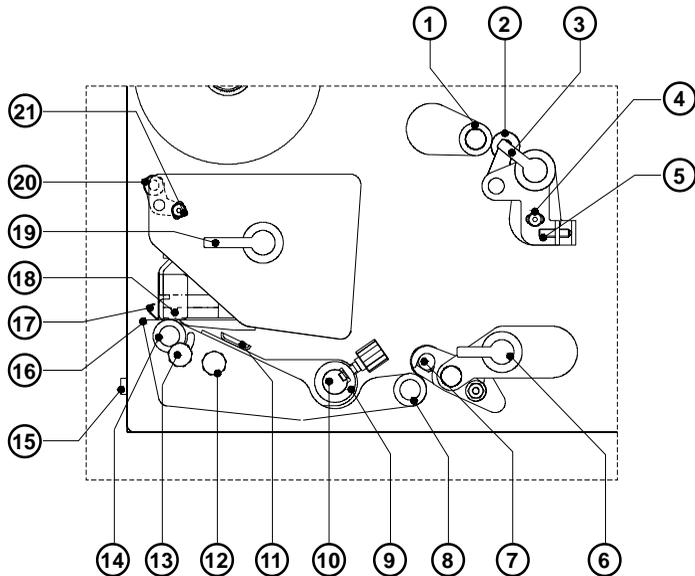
Detailansicht Druckmechanik Hermes 4F/5F
